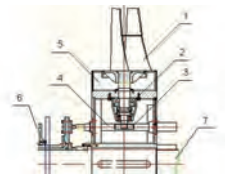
Схема для определения действующей нагрузки на радиально-упорный шарикоподшипник: 1 – лопатки РК, 2 – подшипник, 3 – шестерня, 4 – рейка, 5 – рабочее колесо, 6 – механизм поворота лопаток, 7 – коренной вал
